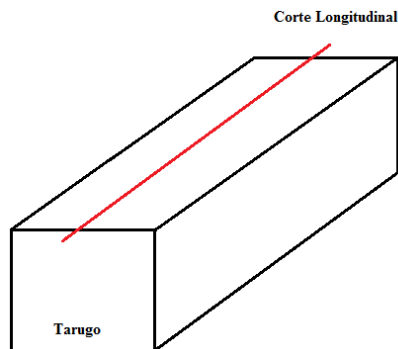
Corte longitudinal da face A do tarugo para análise da espessura da zona coquilhada.
